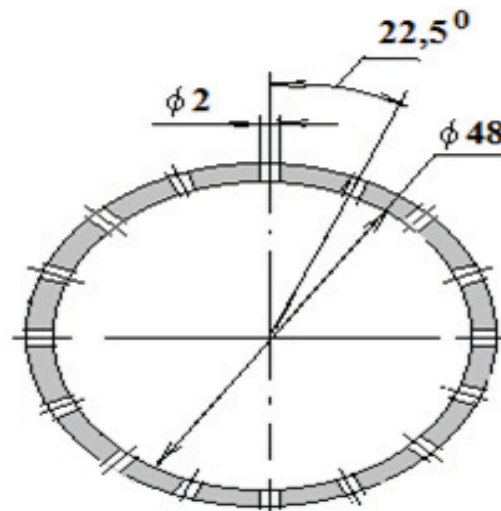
Размеры отверстий в стенке ротора диспергатора
